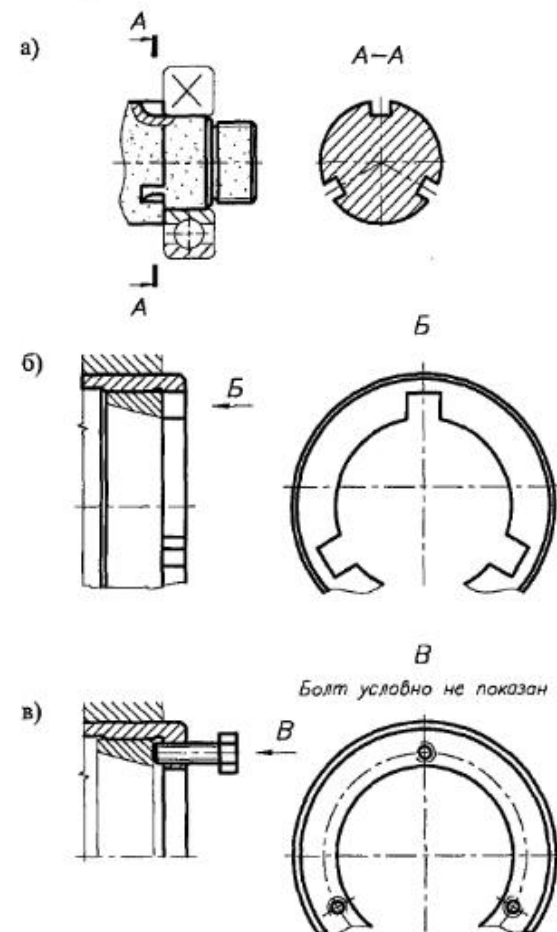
Конструктивные решения по облегчению демонтажа подшипников качения: а), б) выфрезерованные пазы на валу (в корпусе) для возможности захвата лапами съемника боковой поверхности кольца подшипника; в) отверстия с нарезанной резьбой во втулке (корпусе) подшипника для возможности его выжимания из посадочной поверхности.
